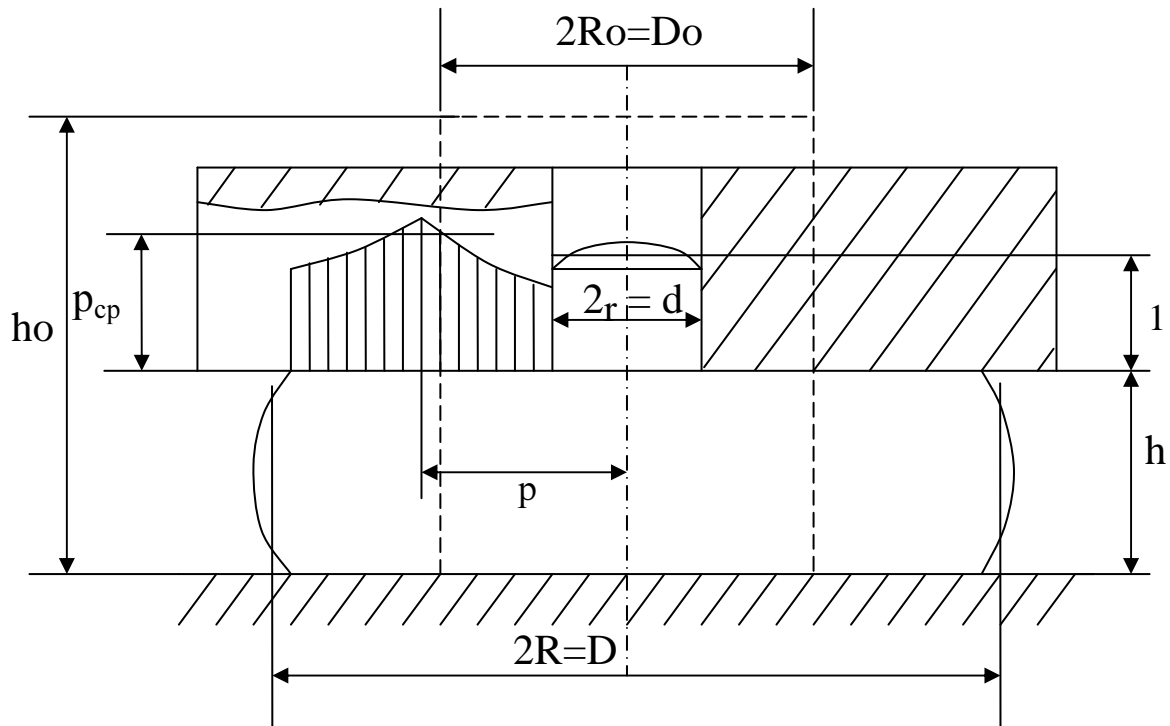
Схема осаджування циліндричного зразка в кільцях
